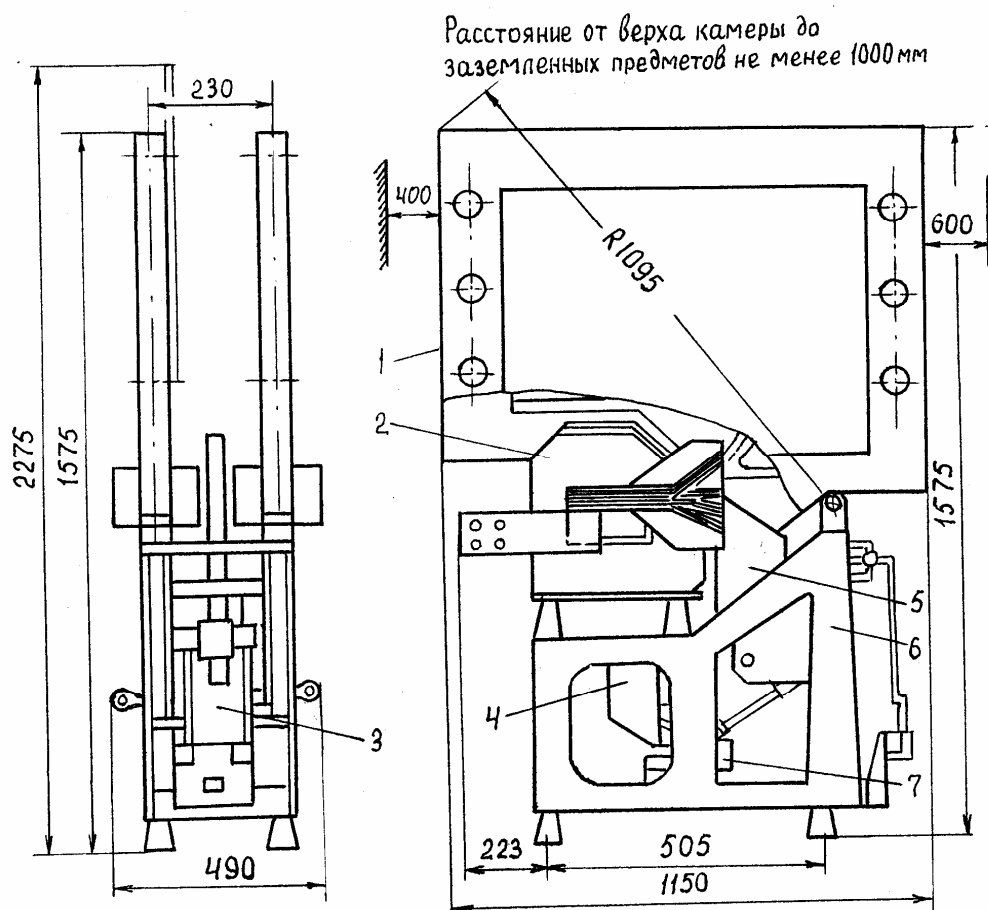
Общий вид быстродействующего выключателя типа ВАБ-28: 1 – камера дугогашения; 2 – неподвижный контакт; 3 – магнитопровод; 4 – якорь; 5 – подвижный контакт; 6 – корпус; 7 – удерживающая катушка
